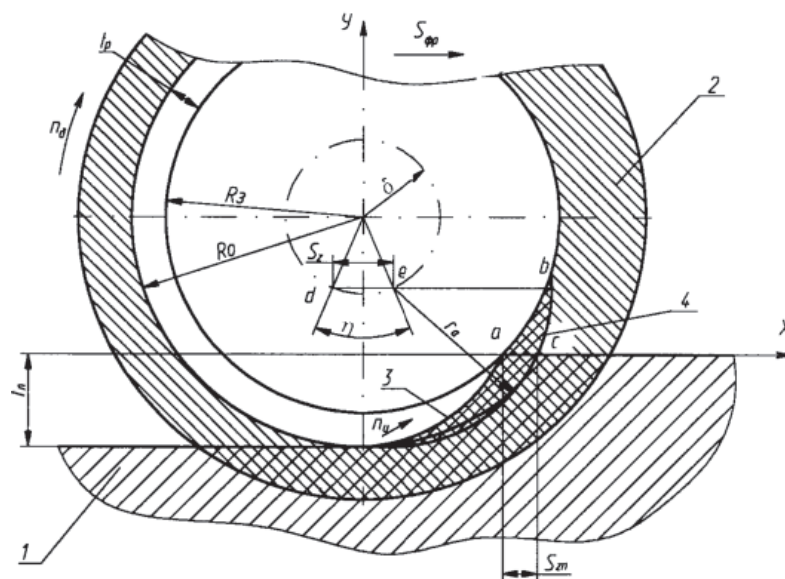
Схема для определения подачи на зуб при фрезероистачивании:
